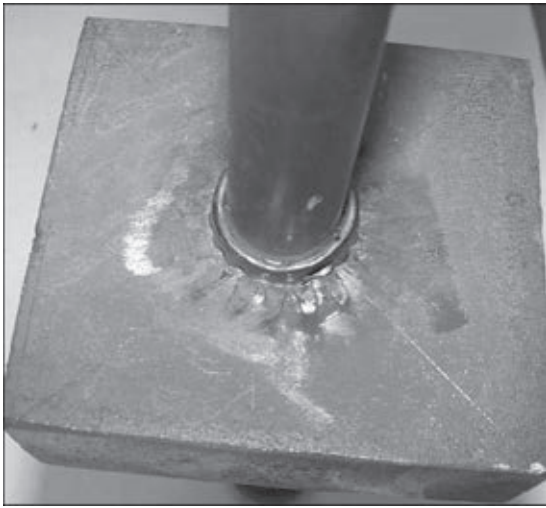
Сварное соединения шпильки с пластиной
